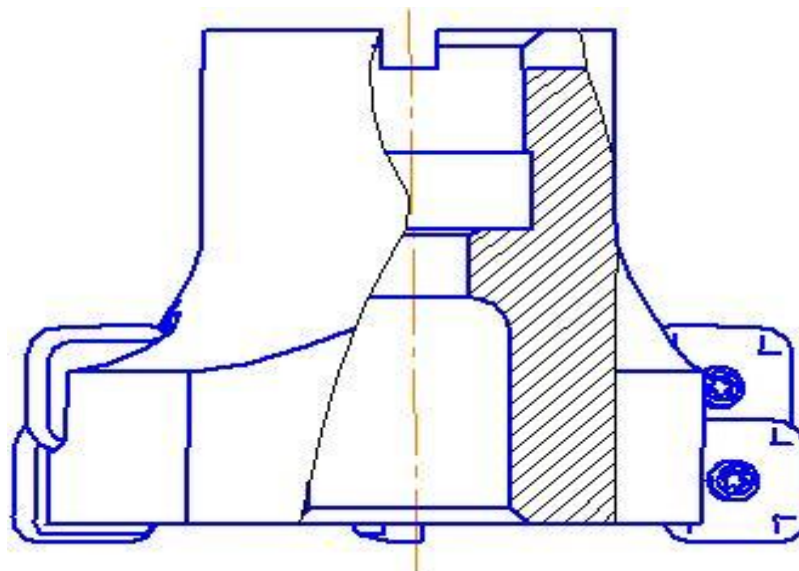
Торцевая фреза с пластинками из твердого сплава.
